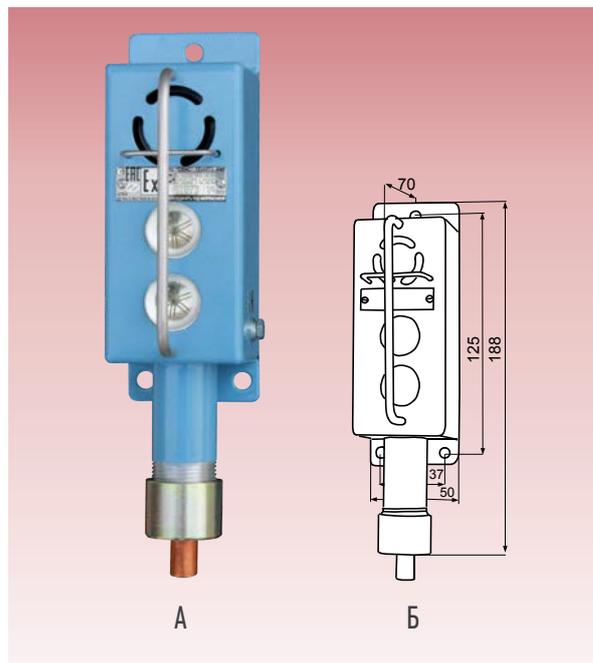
Сигнализатор ВС-3-2СФ-ГС-...: А - внешний вид, Б - габаритные и установочные размеры.
